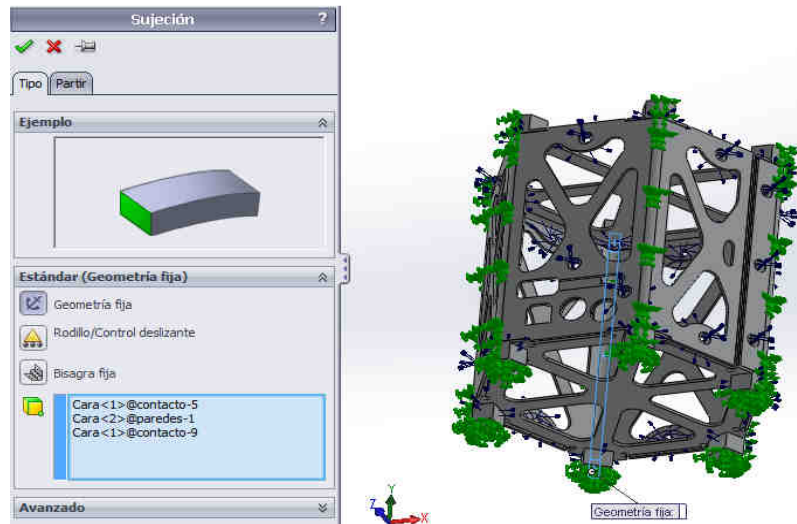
Fijación de los contactos inferiores y aristas de columnas
